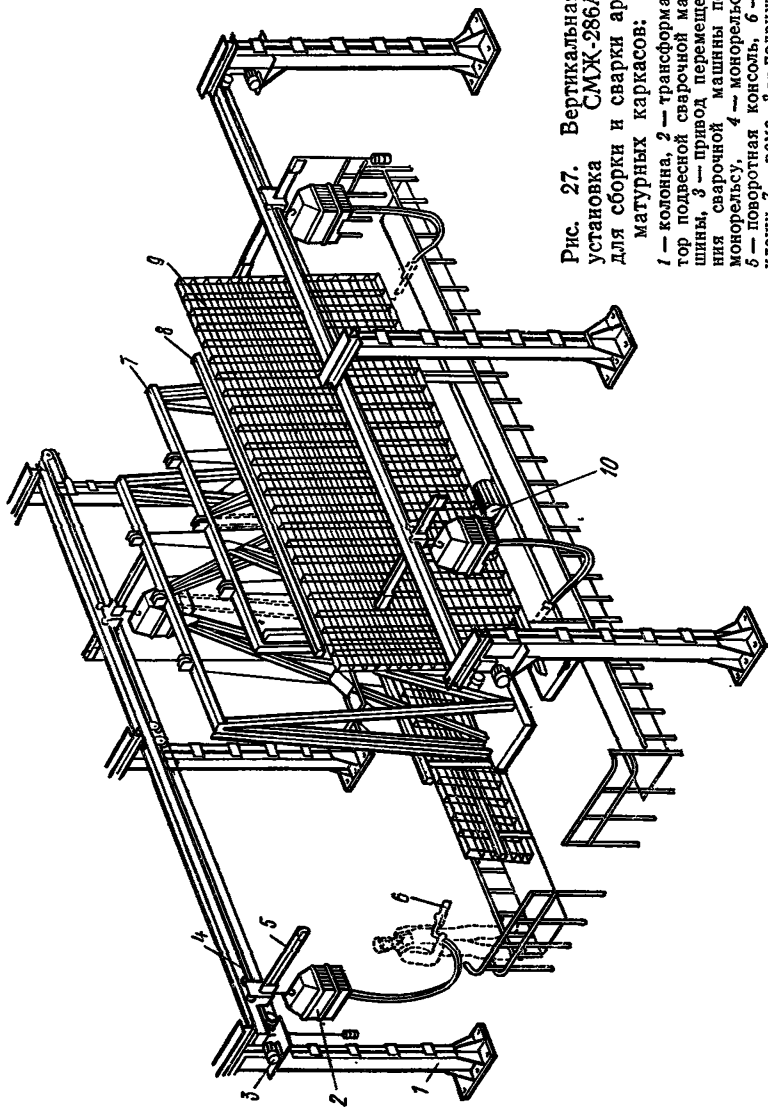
Вертикальная установка СМХ-286А для сборки и сварки арматурных каркасов:
